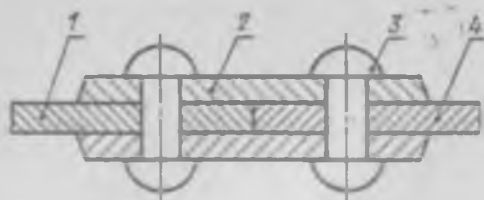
Штриховка и нанесение номеров позиций на сборочных чертежах
